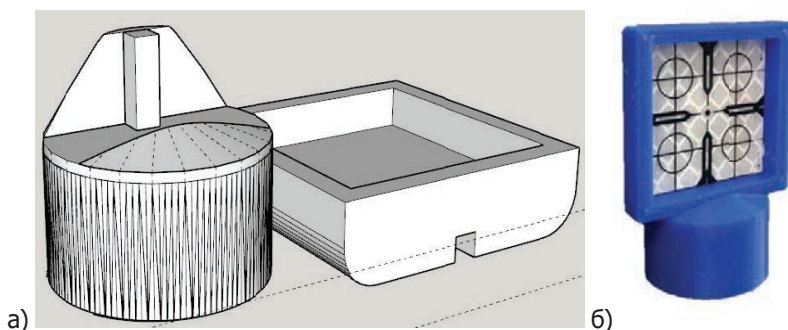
Модель (а) и распечатанный прототип (б) цели – отражателя с резьбой 5 / 8 дюйма
